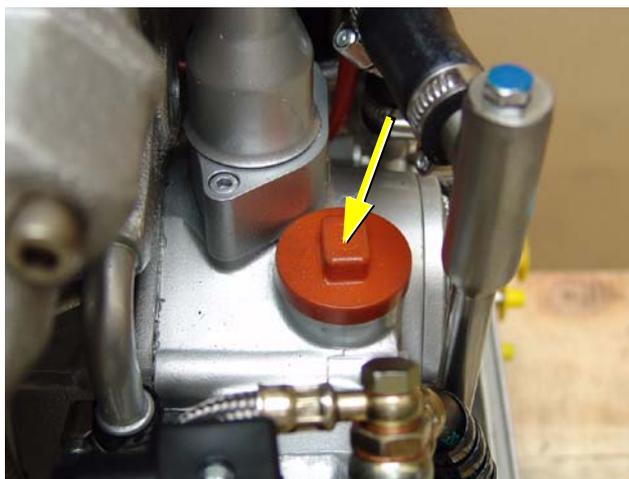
Ouverture du couvercle de remplissage d'huile
